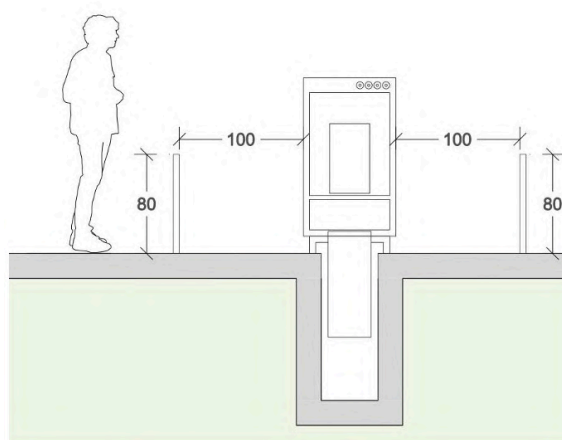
Protección de la maquinaria de corte de piedra con protecciones fijas de perfil de acero colocado en la solera de hormigón existente
